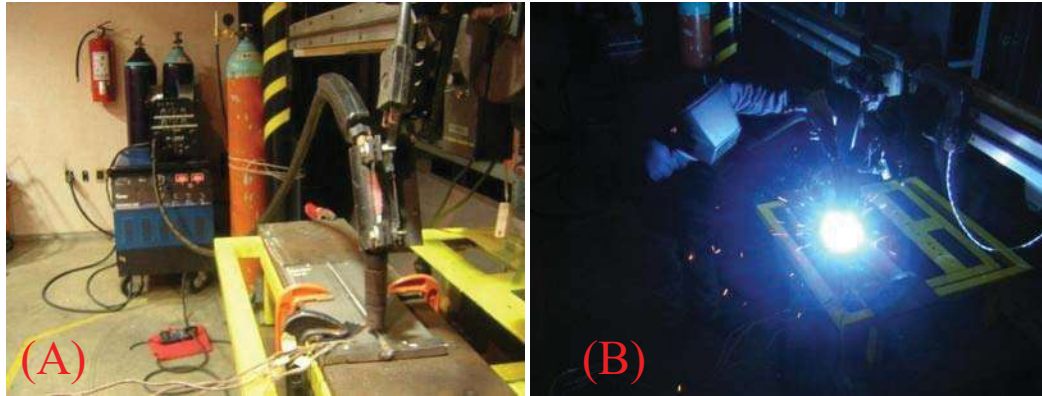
8 (A) Montaje de placas y puesta a punto de la maquina. (B) Soldadura de las placas de acero dúplex 2205.
